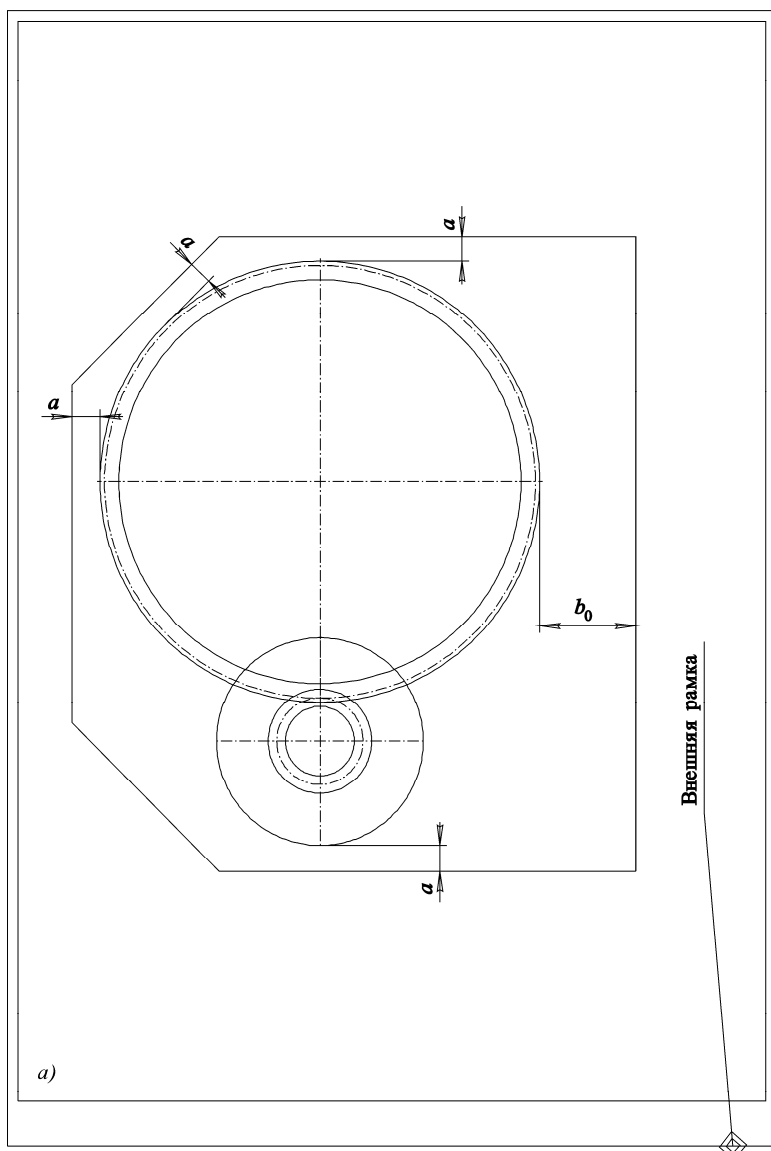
Пример эскизной компоновки зубчатого цилиндрического одноступенчатого редуктора:
